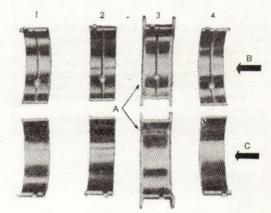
Cojinetes de apoyo del cigüeñal.
